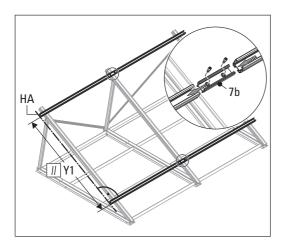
Montaggio delle guide dei profili di montaggio, passaggio 1
